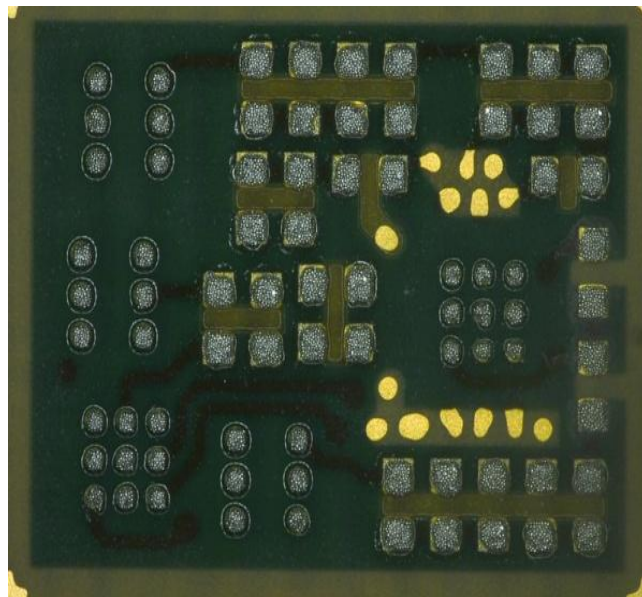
Impresión de soldadura de pasta usando soldadura tipo V
